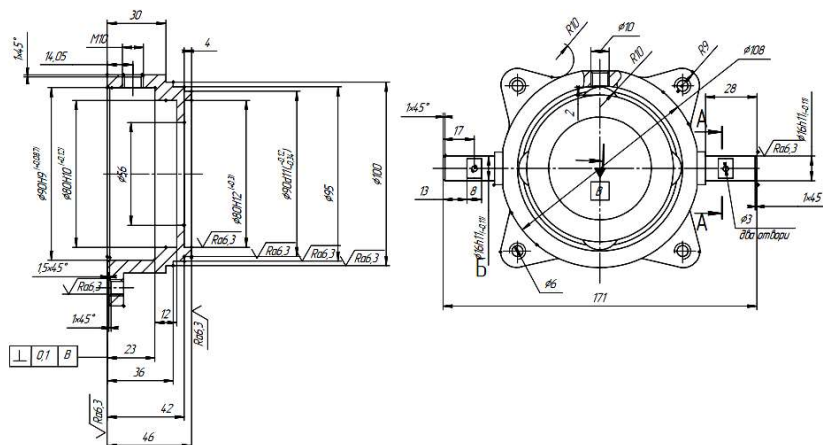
Загальний вигляд деталі «Корпус БМД 6.404»
